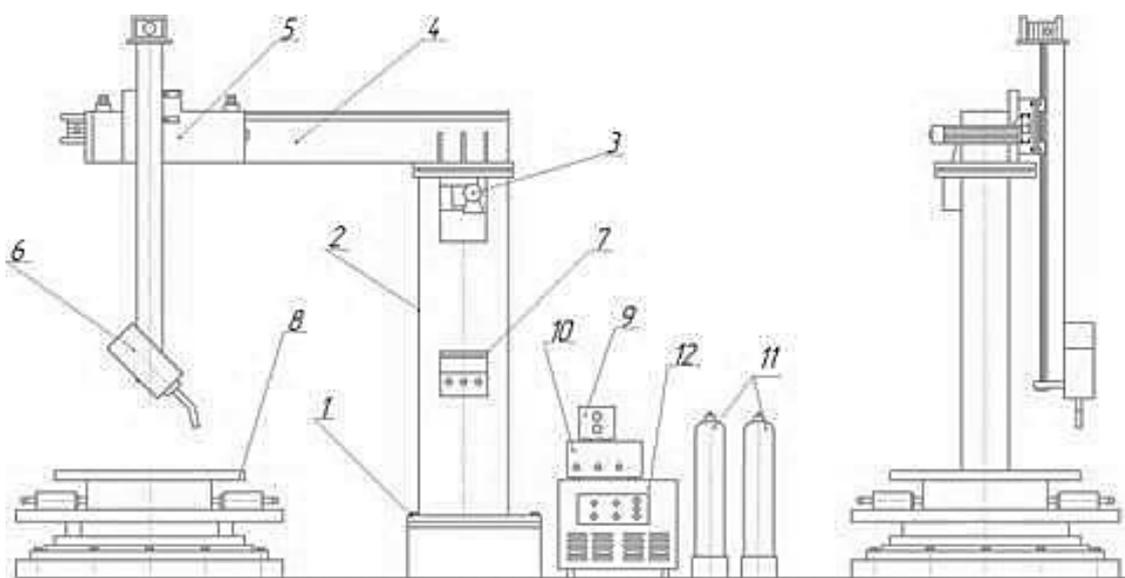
Сварочная автоматическая установка (УН-2ГС):
